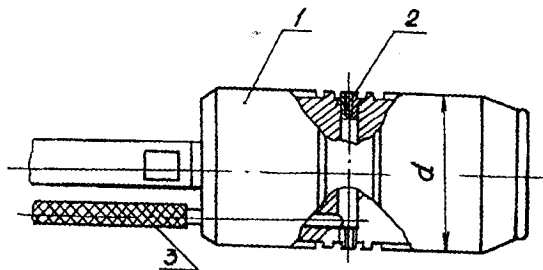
Пневматичний калібр для вимірювання діаметра та відхилення поперечного перерізу
